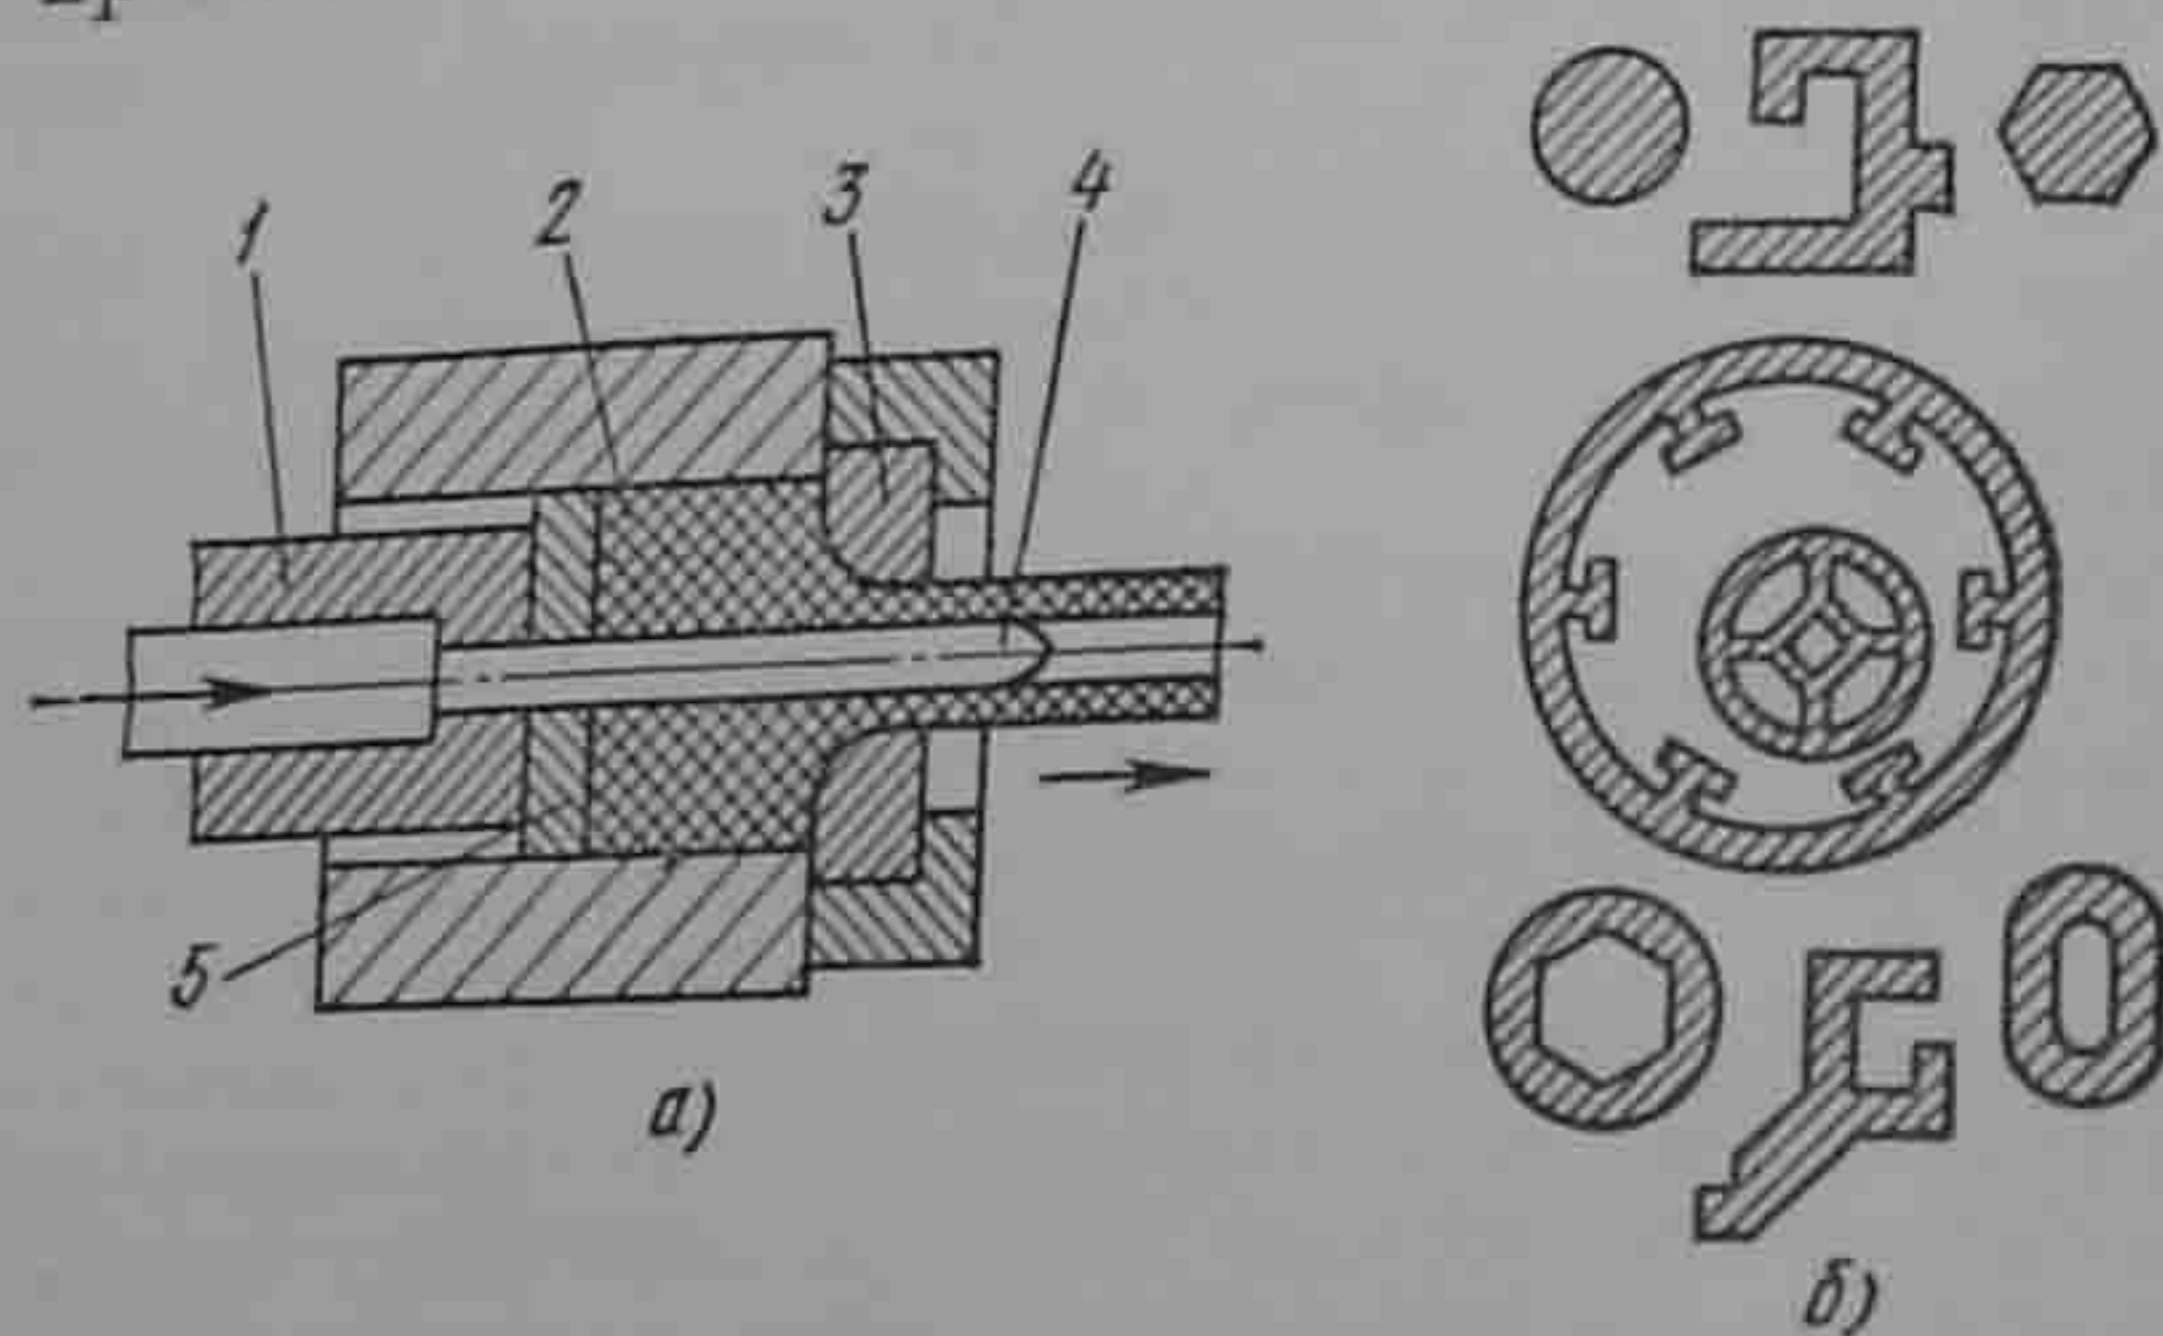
Схема прессования полого профиля (а) и примеры прессованных профилей (б)
